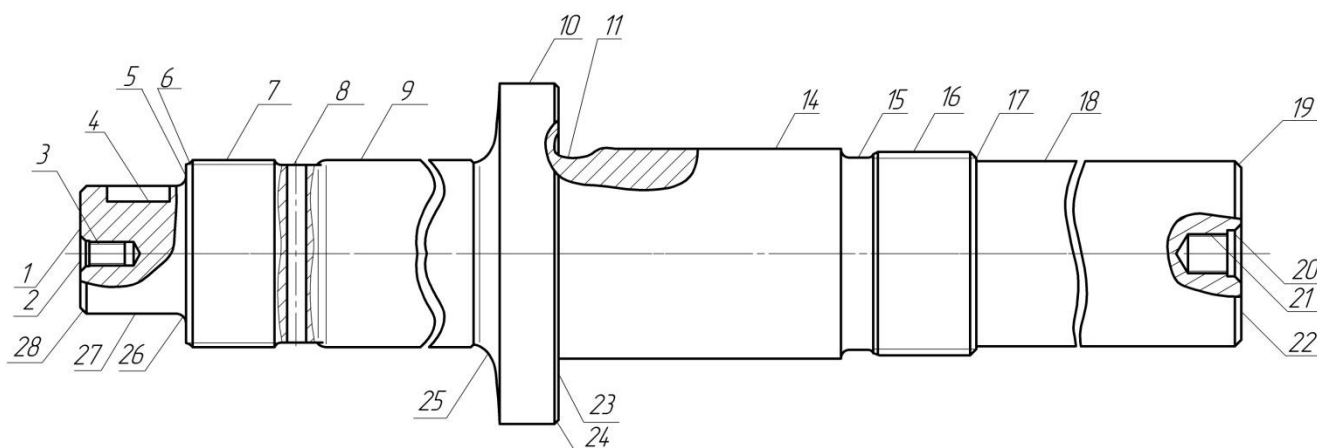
Нумерація поверхонь деталі Вал ведучий
